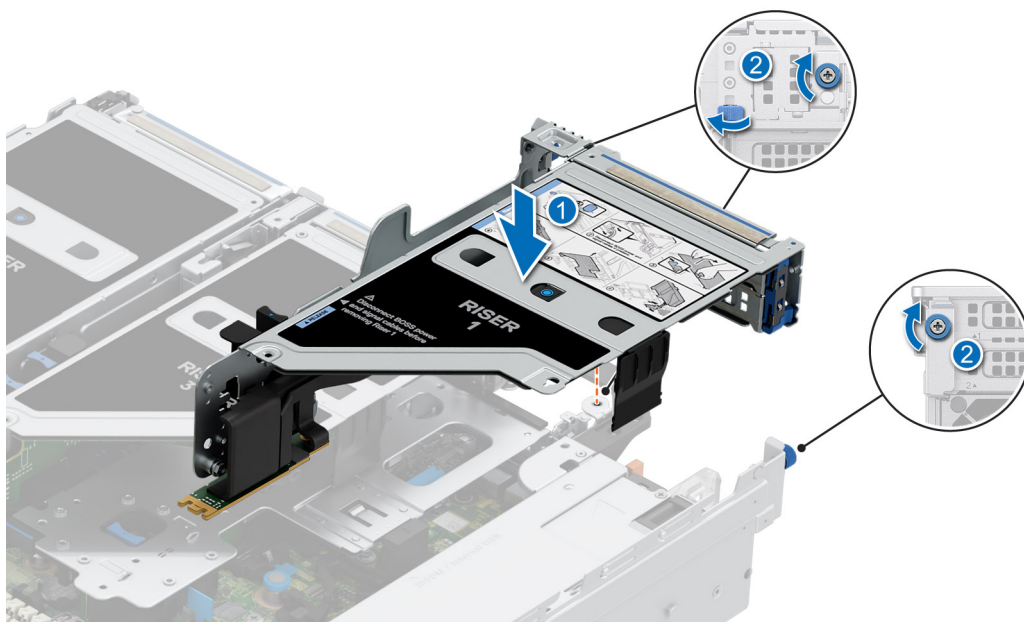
Installation de la carte de montage pour carte d'extension (carte de montage 1)
